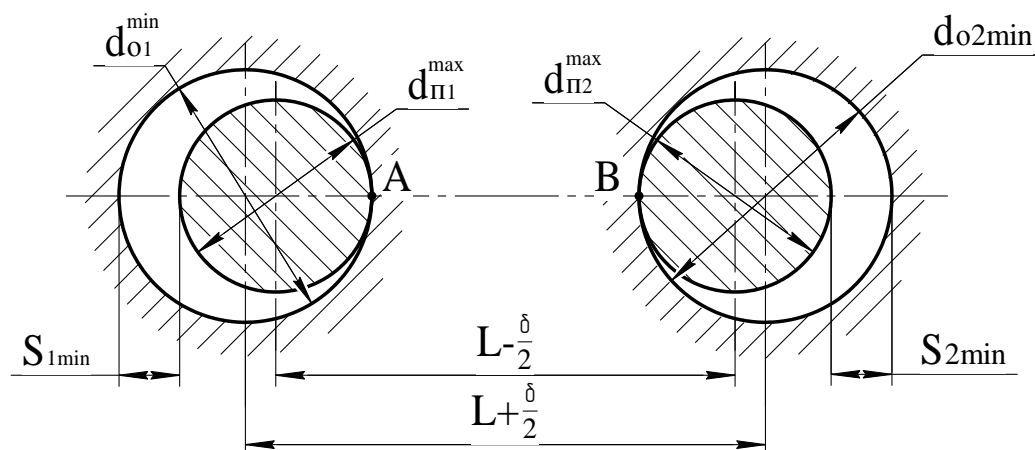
Схема установки заготовки на два цилиндрических пальца
